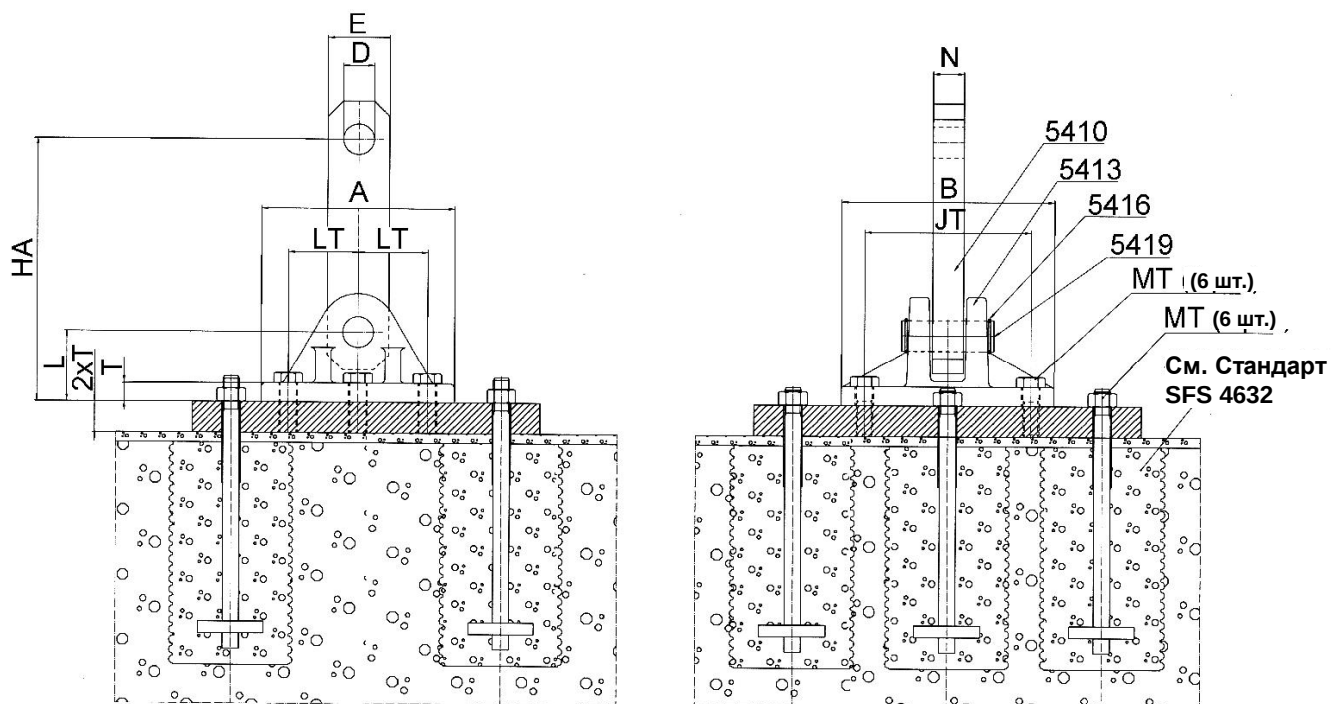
Детали и размеры реактивной штанги, размеры 100-160
